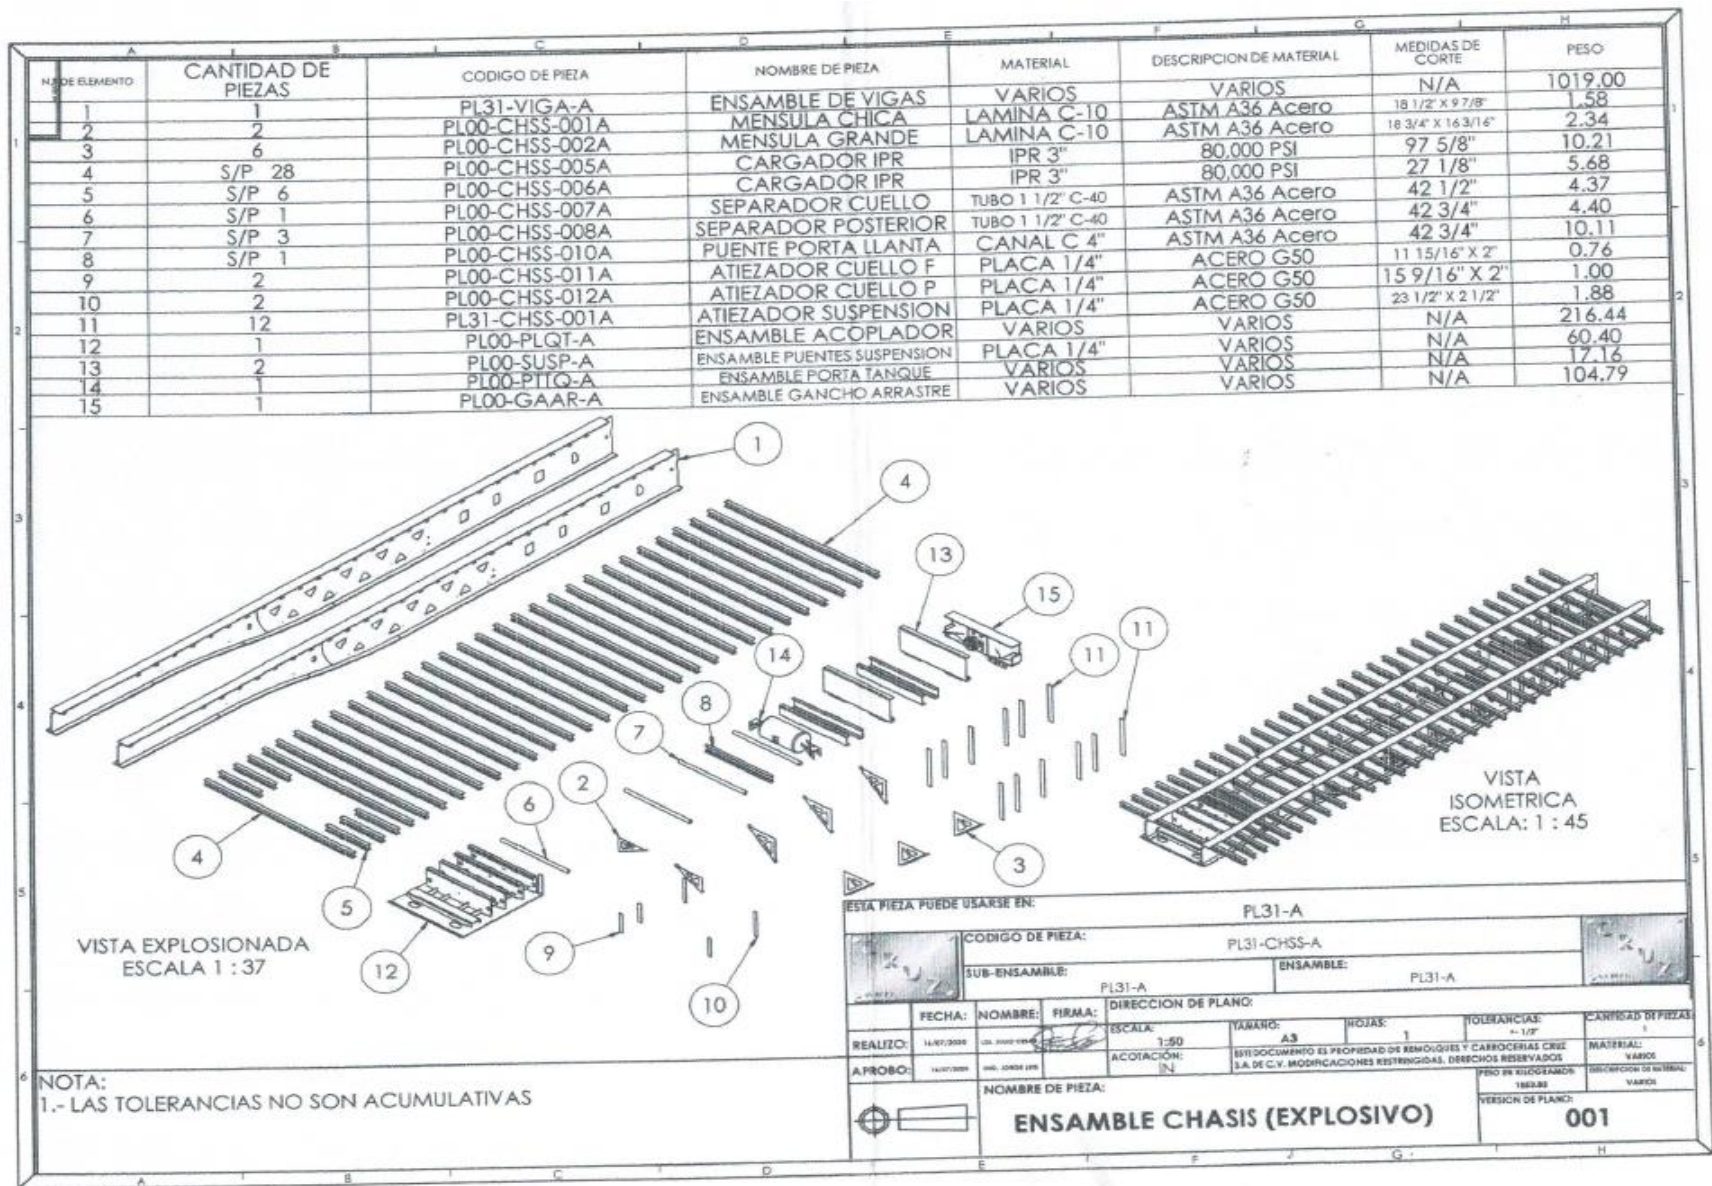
Plano del ensamble del chasis (explosivo). Fuente: Remolques y Carrocerías Cruz, S.A. de C.V., 2020.
